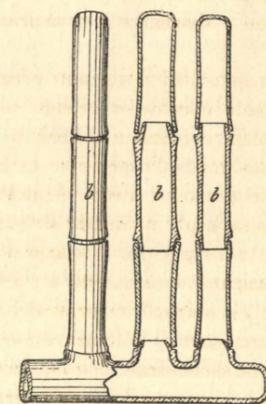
FIG. D. — Prospetto e sezione dei tubi in porcellana d'amianto.
